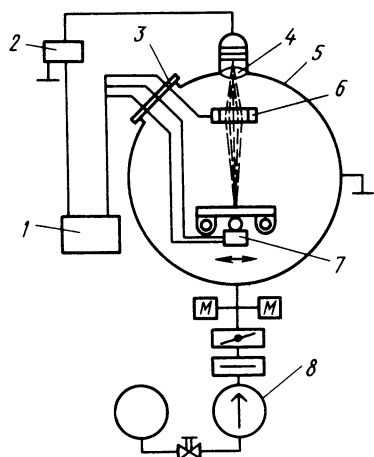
Сварочная электронно-лучевая установка:
